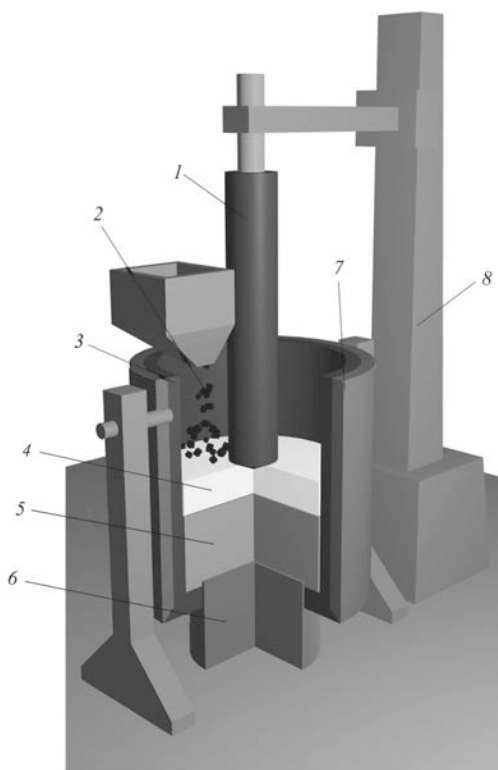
Схема електрошлакового наплавлення міді на сталь: 1 — графітовий електрод; 2 — мідна присадка; 3 — графітовий тигель; 4 — шлакова ванна; 5 — металева ванна; 6 — сталева заготовка; 7 — теплоізоляція; 8 — колонна
